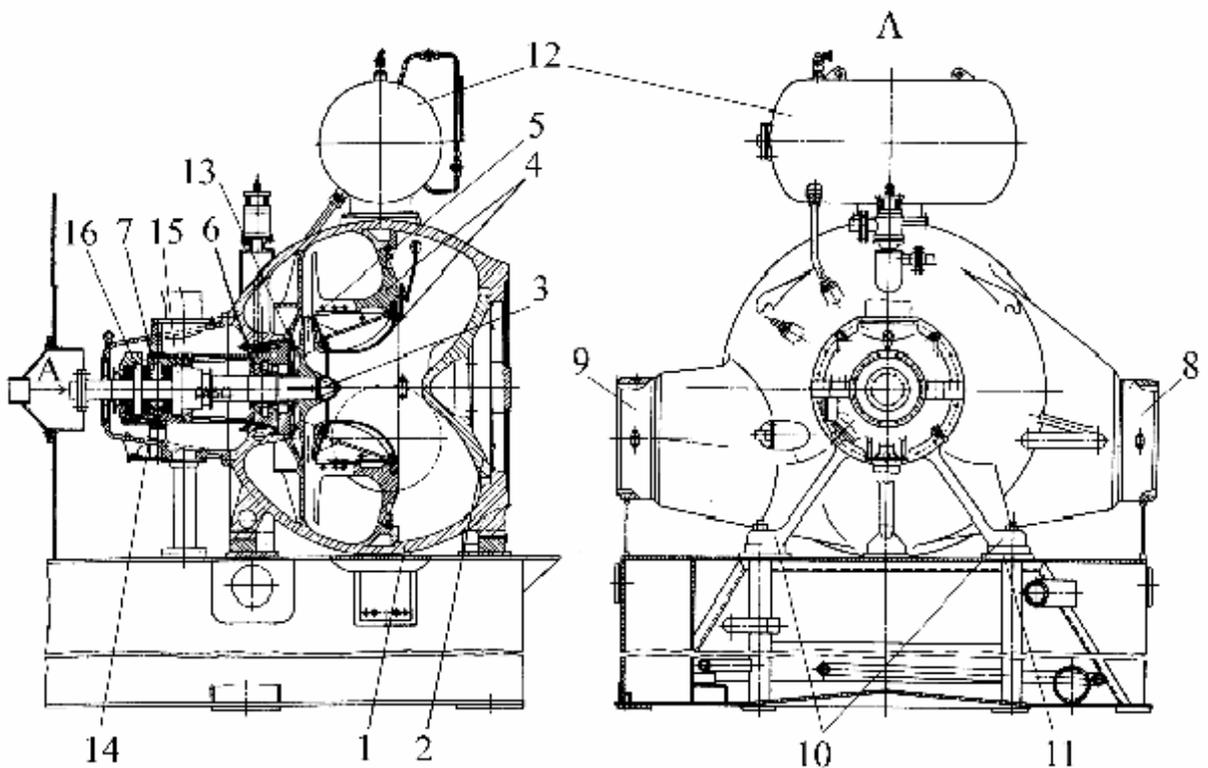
Одноступенчатый центробежный компрессор конструкции НЗЛ
